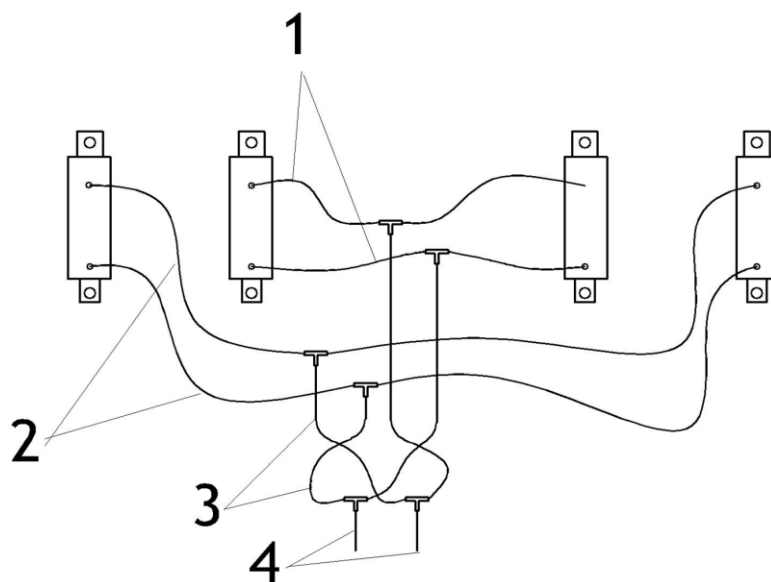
Système hydraulique de réglage de la profondeur de travail TOP 4,0-4,8 : 1- tuyau hydraulique 1 m (4 pcs), 2- tuyau hydraulique 1,7 m (4 pcs), 3- tuyau hydraulique 1,8 m (4 pcs) 4- tuyau hydraulique 1 m (2 pcs).
